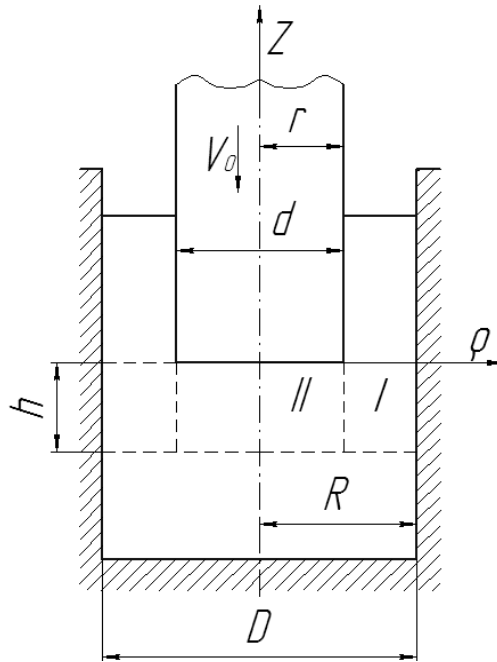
Розрахункова схема зворотного видавлювання
